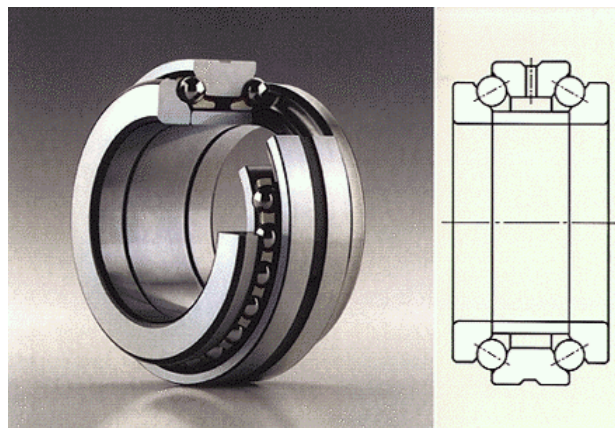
Rodamiento axial de bolas de contacto angular de doble efecto
